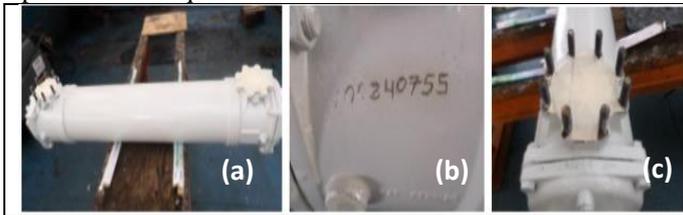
(a) Resfriador de Óleo. Equipamentos devidamente reconicionados, conforme especificações técnicas, testados e embalados, prontos para aplicação no motor.
